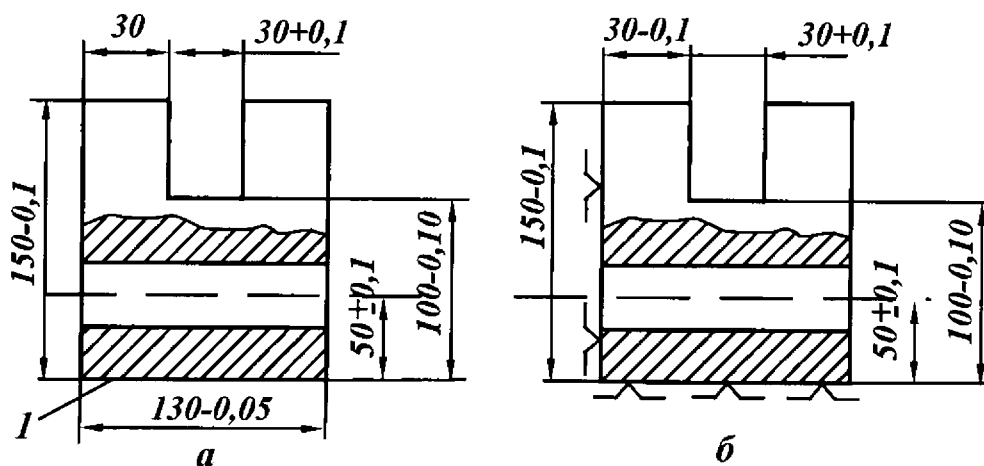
Чертеж детали (*а*) и операционный эскиз (*б*)
